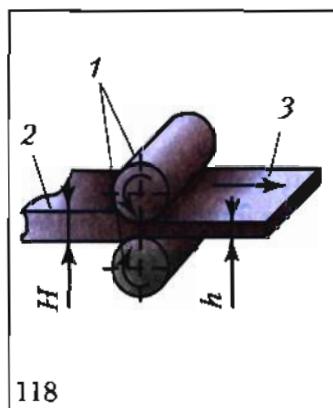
Получение металлического листа прокаткой: 1 – валки; 2 – заготовка; 3 – лист
